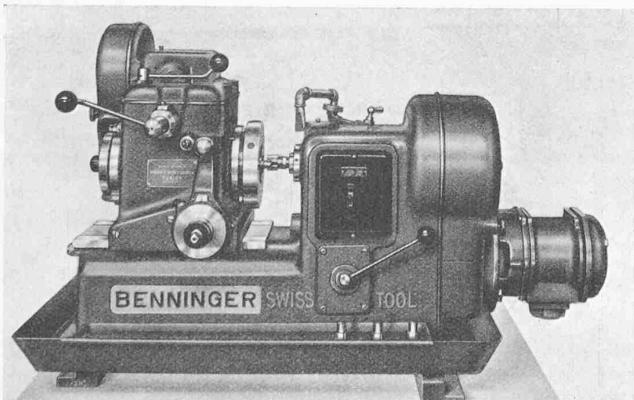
«Benninger» Kurzgewinde-Fräsmaschine
